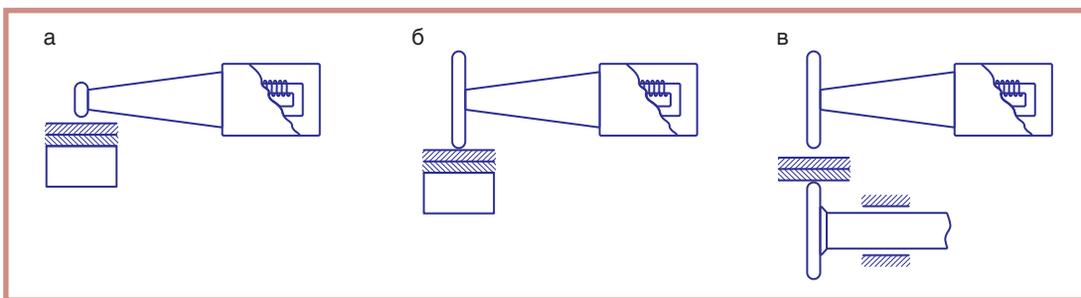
Варианты построения механических колебательных систем для шовной сварки
